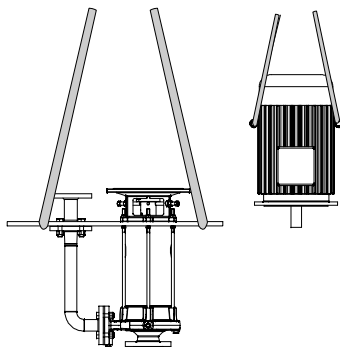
Транспортировка насоса и двигателя, начиная с размера двигателя 180
